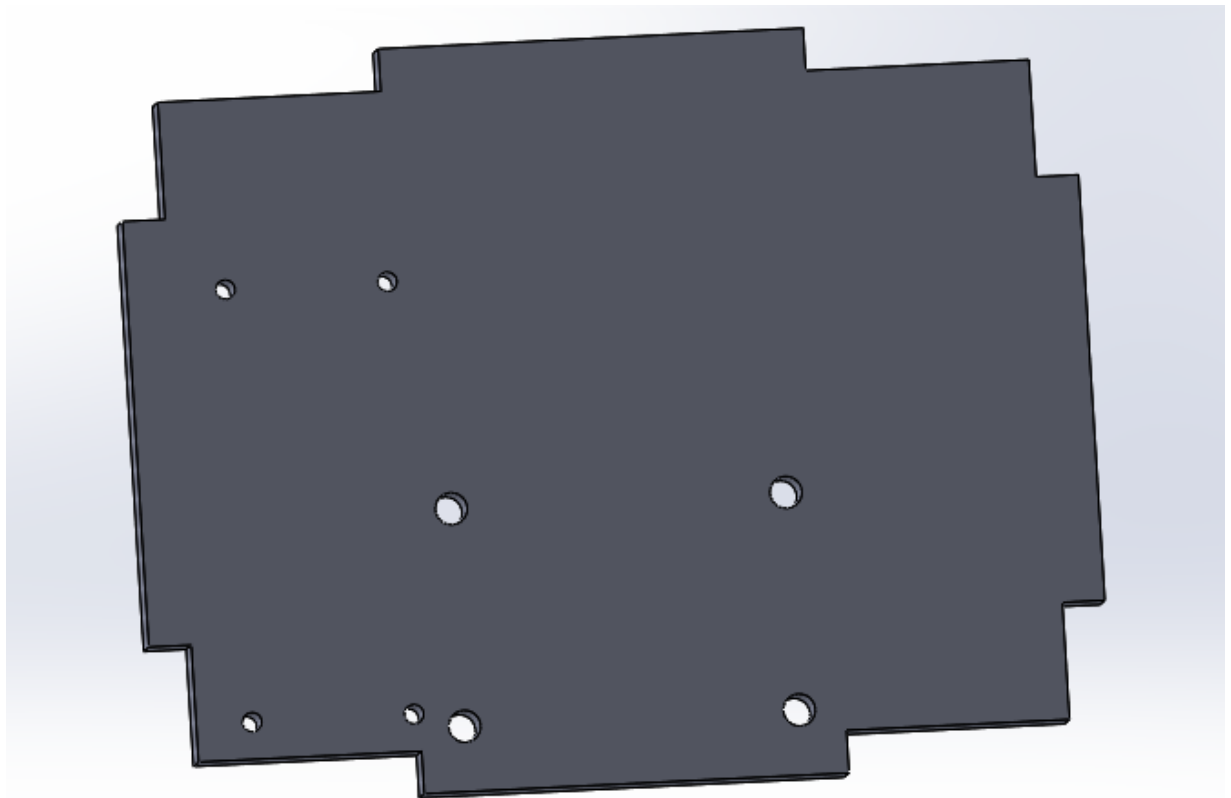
деталь основи корпусу з отворами для кріплення плат
